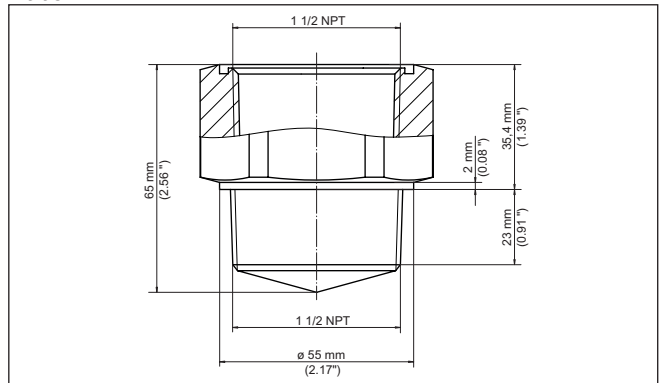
Maße Gewindeadapter 1½ NPT auf Gewinde 1½NPT
